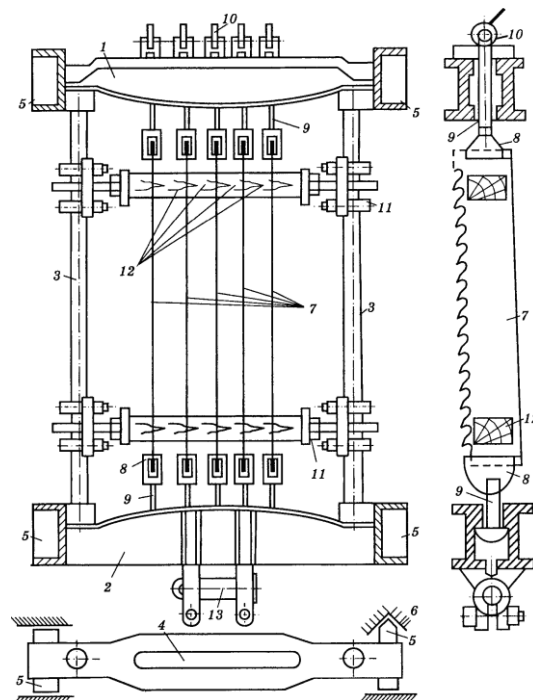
Пилкова рамка: 1 – поперечина; 2 – поперечина нижня; 3 – стійки; 4 – паз; 5 – повзун; 6 – напрямні; 7 – пилки; 8 – захопи; 9 – підвіски; 10 – натяжний пристрій; 11 – струбцини; 13 – палець
